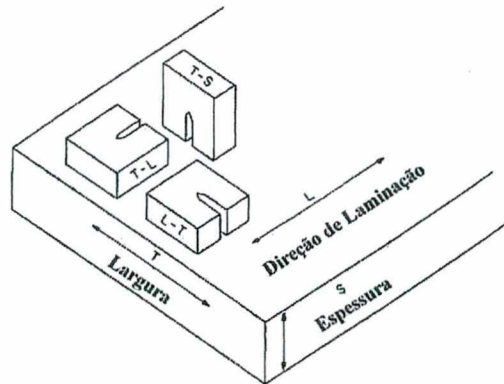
Representação das posições de retirada dos corpos de prova para os ensaios de impacto na junta soldada.
